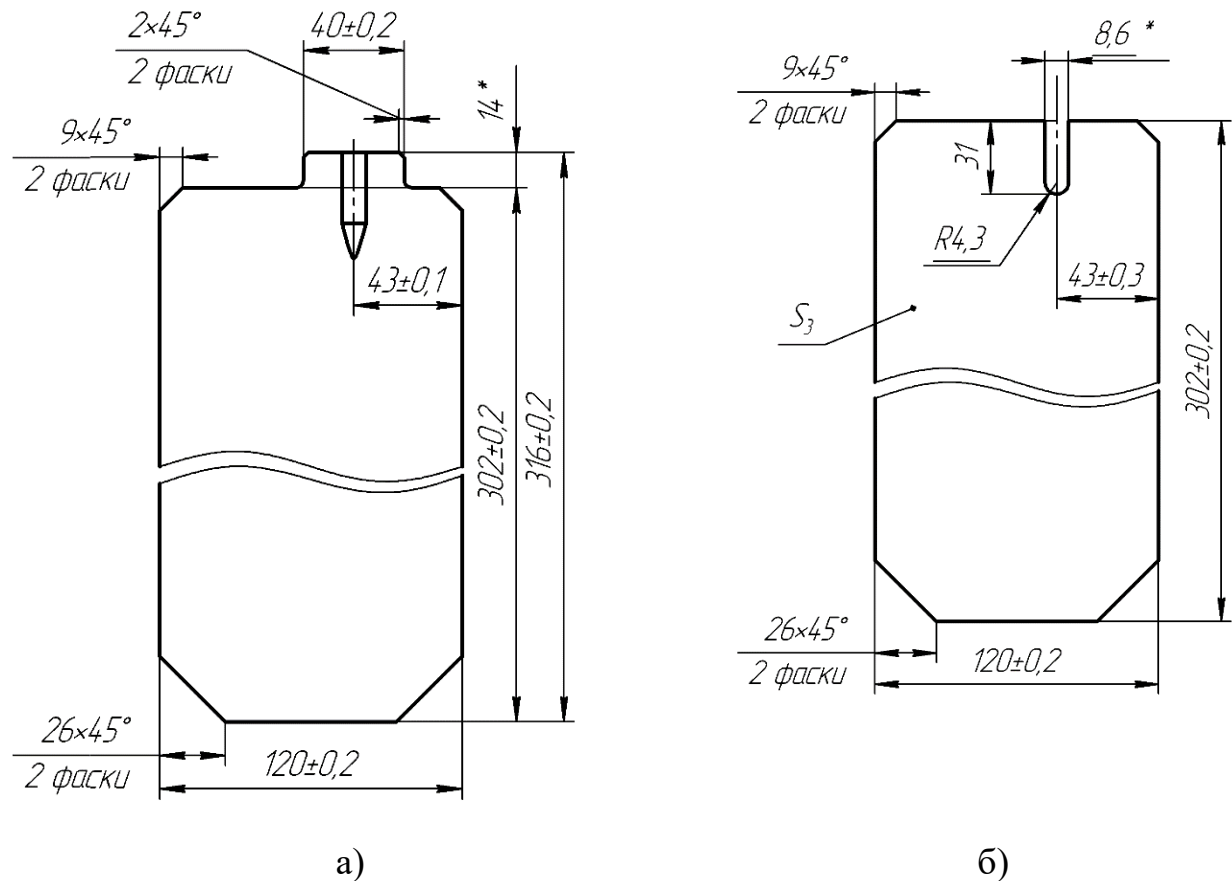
Форма заготовок: а) заготовка обшивки; б) заготовка наповнювача
